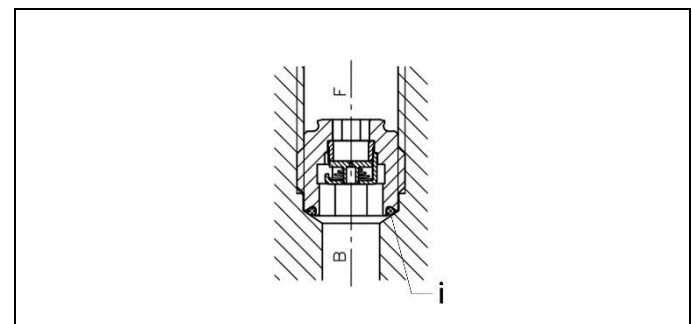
Clapet anti-retour d'orifice - variantes d'installation
